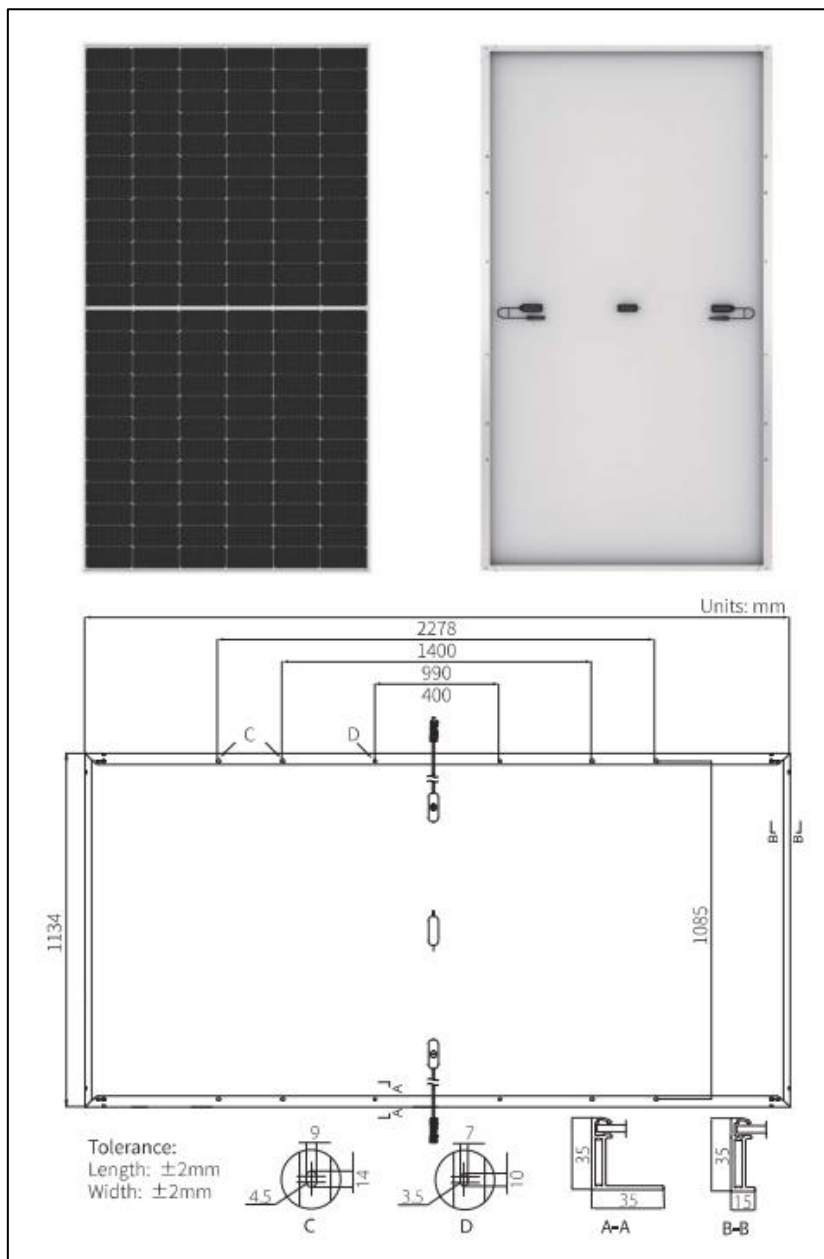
Dimensiones del módulo LR5-72HPH-540M [47].
